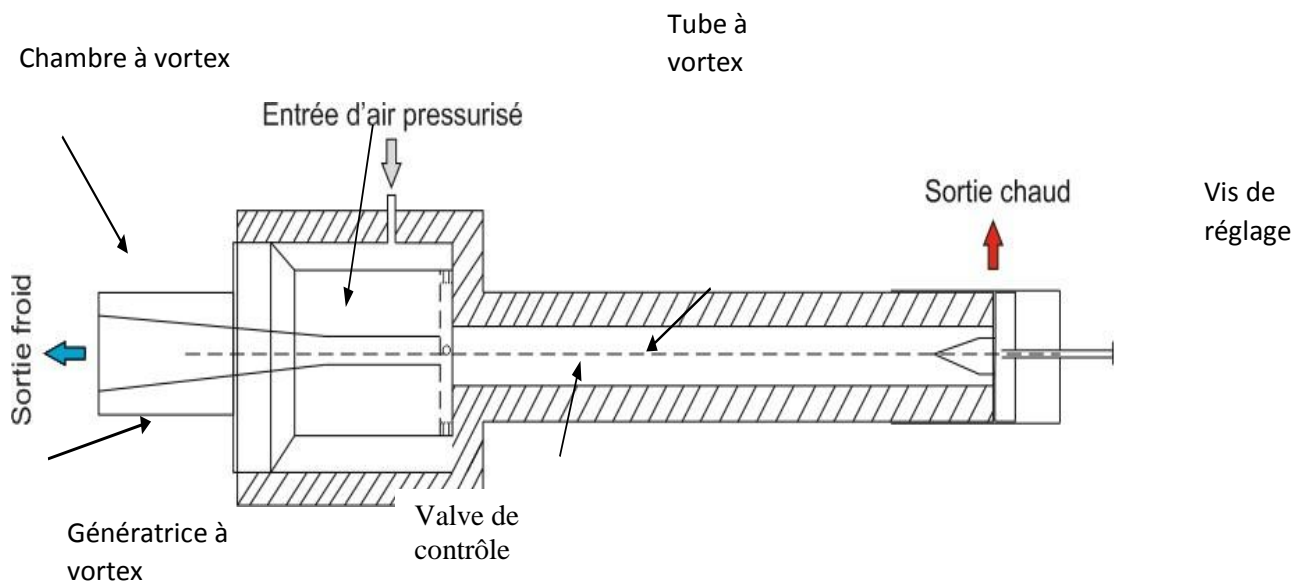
schéma de l'assemblage du tube a vortex.
